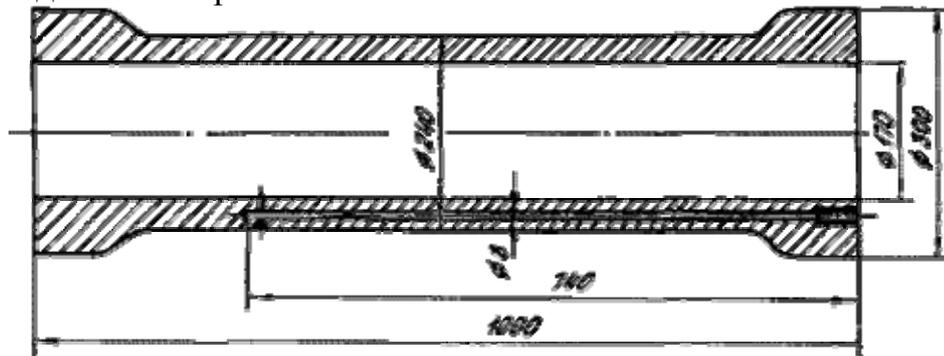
Пример нетехнологичной конструкции корпуса гидравлического цилиндра
